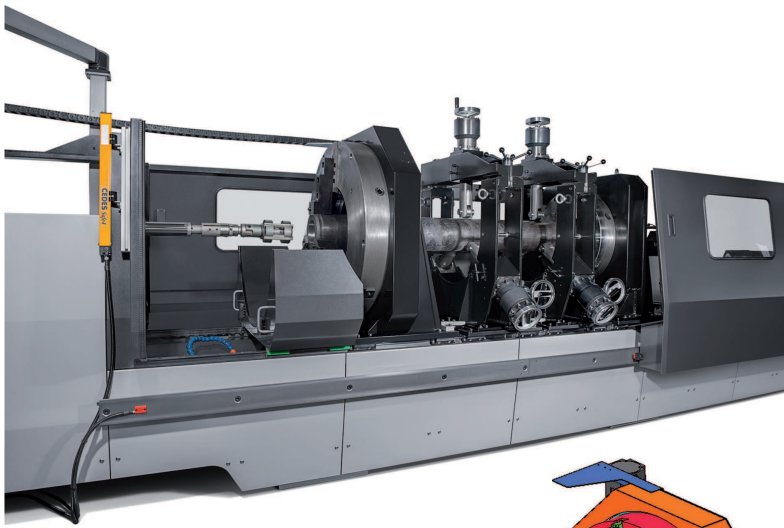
Das Honwerkzeug (links) bearbeitet in dieser Anwendung die Innenfläche eines Rohres (rechts).
